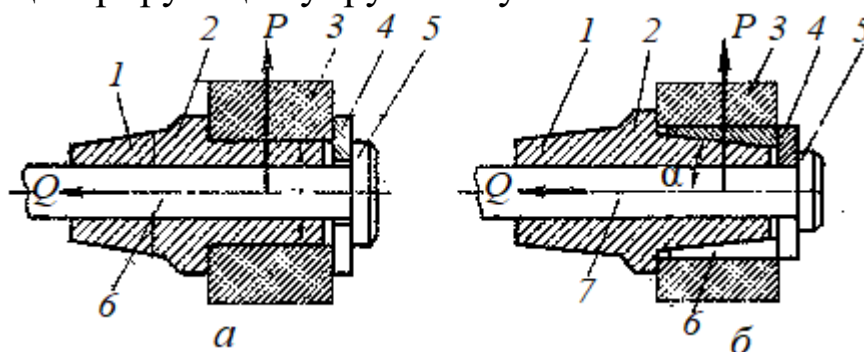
Конструкции оправок: *а* – гладкая оправка; *б* – оправка с разрезной втулкой
